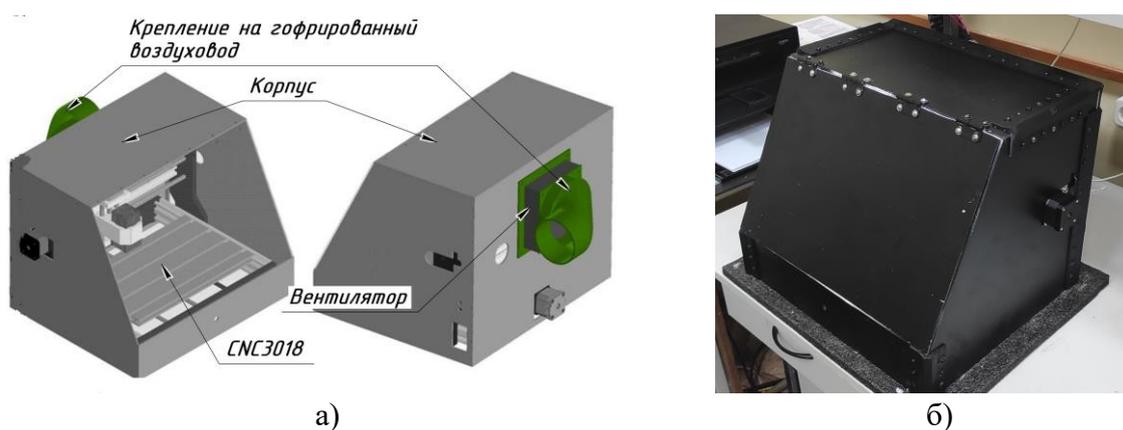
Внешний корпус фрезерного ЧПУ станка CNC 3018 в виде 3D-модели (а) и в реальном исполнении (б).
